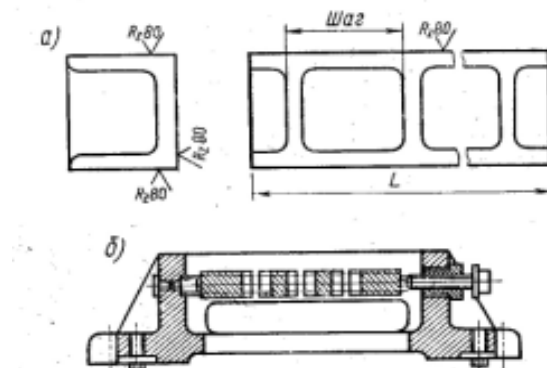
Заготовка корпусу пристосування з швелера (а) і використання його в пристосуванні (б)
